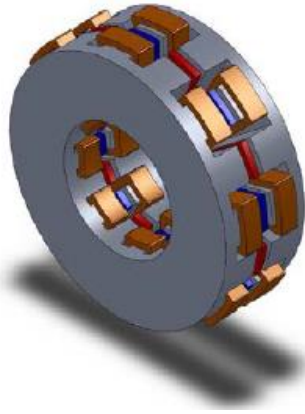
Máquinas de rotor interior con rotor sin núcleo
